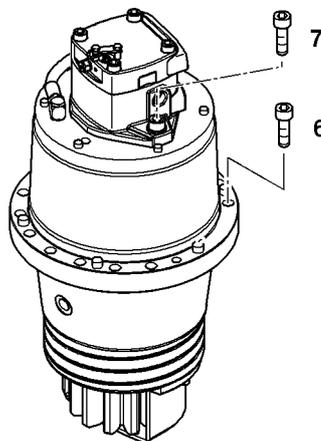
Tornillos de fijación uniendo la caja y el motor del mecanismo giratorio
